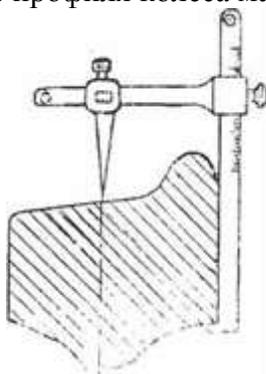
Измерение толщины обода колеса толщиномером стандартного профиля вагонного колеса по ГОСТ 9036-76 (рисунок 4).
